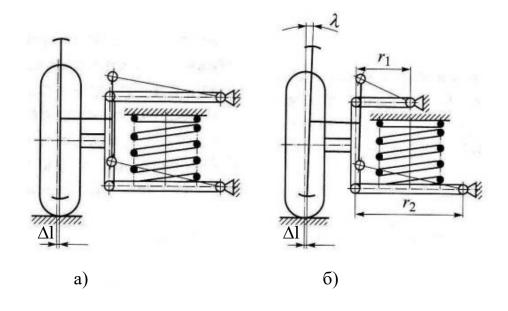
Схемы двухрычажных подвесок с рычагами одинаковой (а) и разной (б) длины
